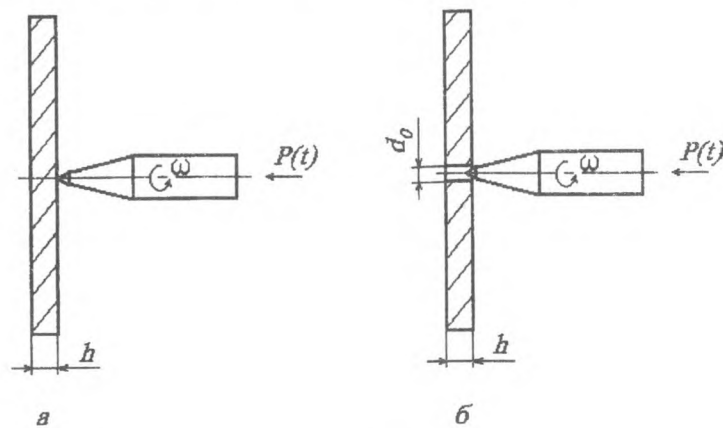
Схемы обработки: а — стенка без отверстия; б — стенка с предварительным отверстием
